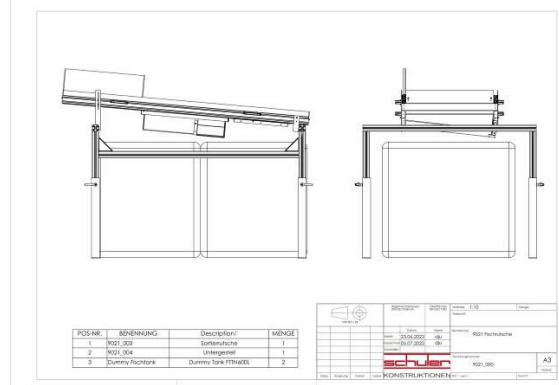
Sortierrutsche mit den modularen Erweiterungen
